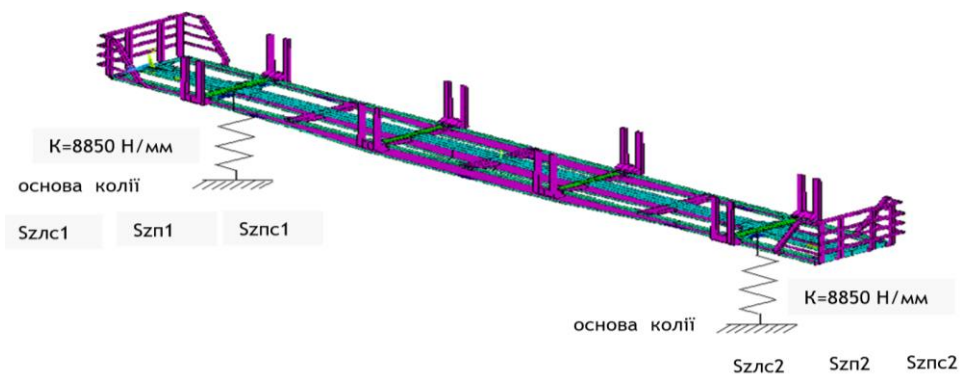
Розрахункова схема для моделювання напружено-деформованого стану довгобазного вагона-платформи під час руху по залізничній колії.
